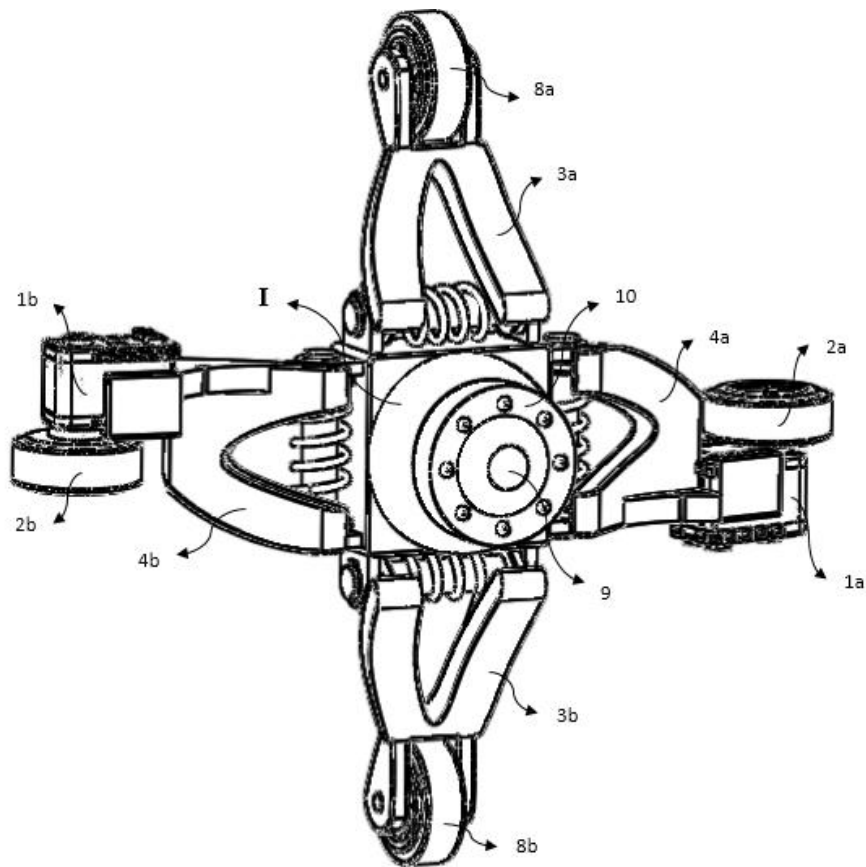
Diseño CAD del robot. Sección frontal I. (Vista isométrica)
